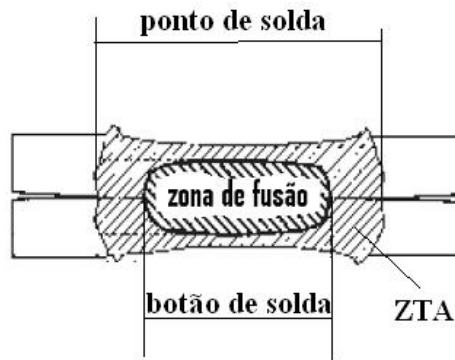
Esquemática de botão e ponto de solda (Ruiz, 2005)
